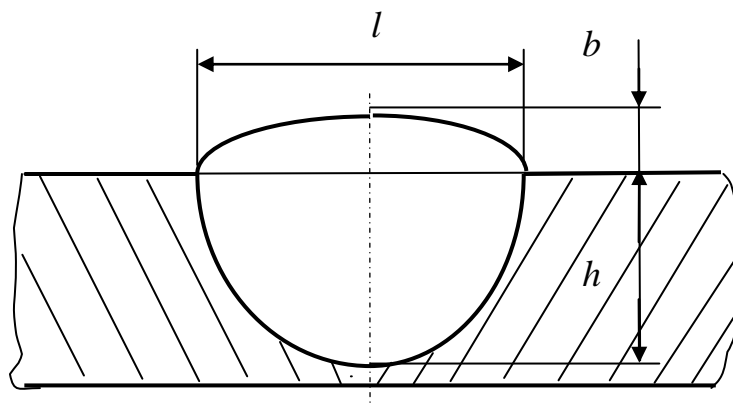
Розміри зварного шва:  $l$ -ширина шва,  $b$  – висота посилення шва,  $h$  – глибина проплавлення металу
